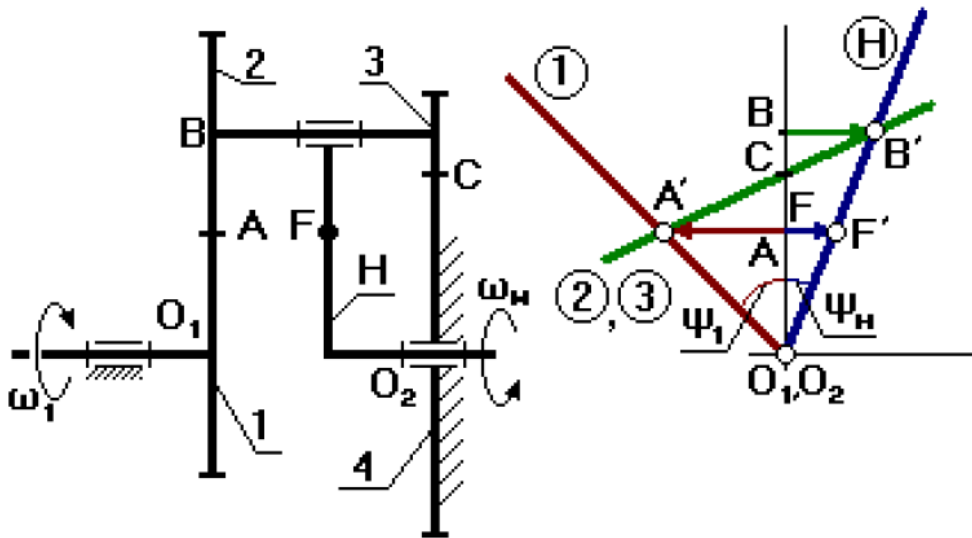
Редуктор Давида: 1,2 – внешняя зубчатая пара, 3 – колесо, 4 – коронная шестерня, H - водило
